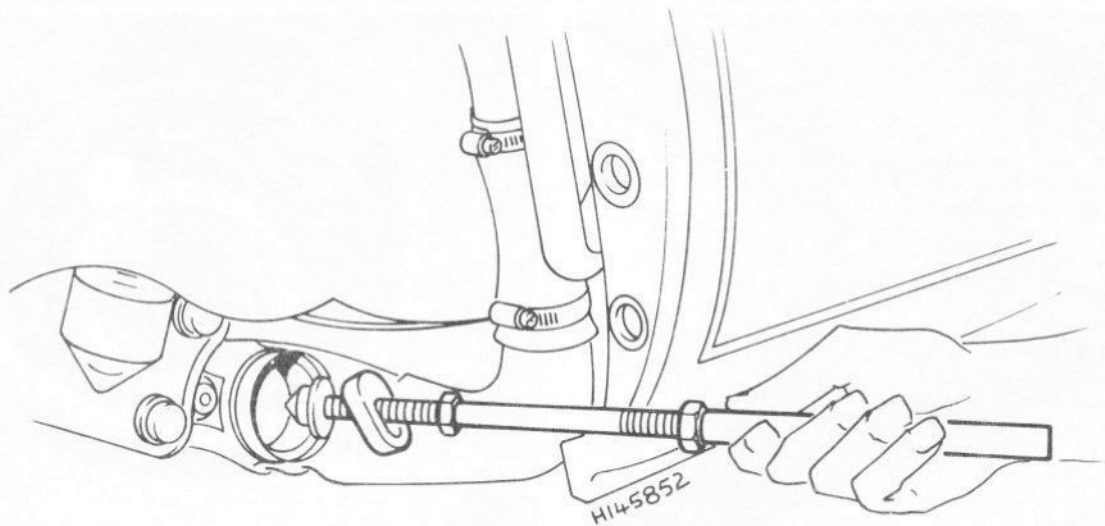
Outil Peugeot 70526 de dépose des paliers de bras de suspension arrière (Sec 14)
